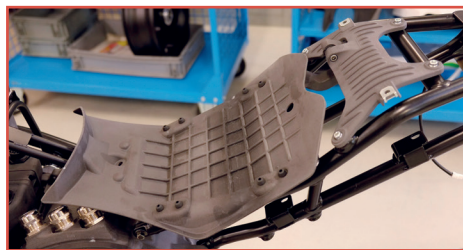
Prototipo funzionale del telaio (o base sella) in stampa 3D e Windform® GT. Prove di montaggio
